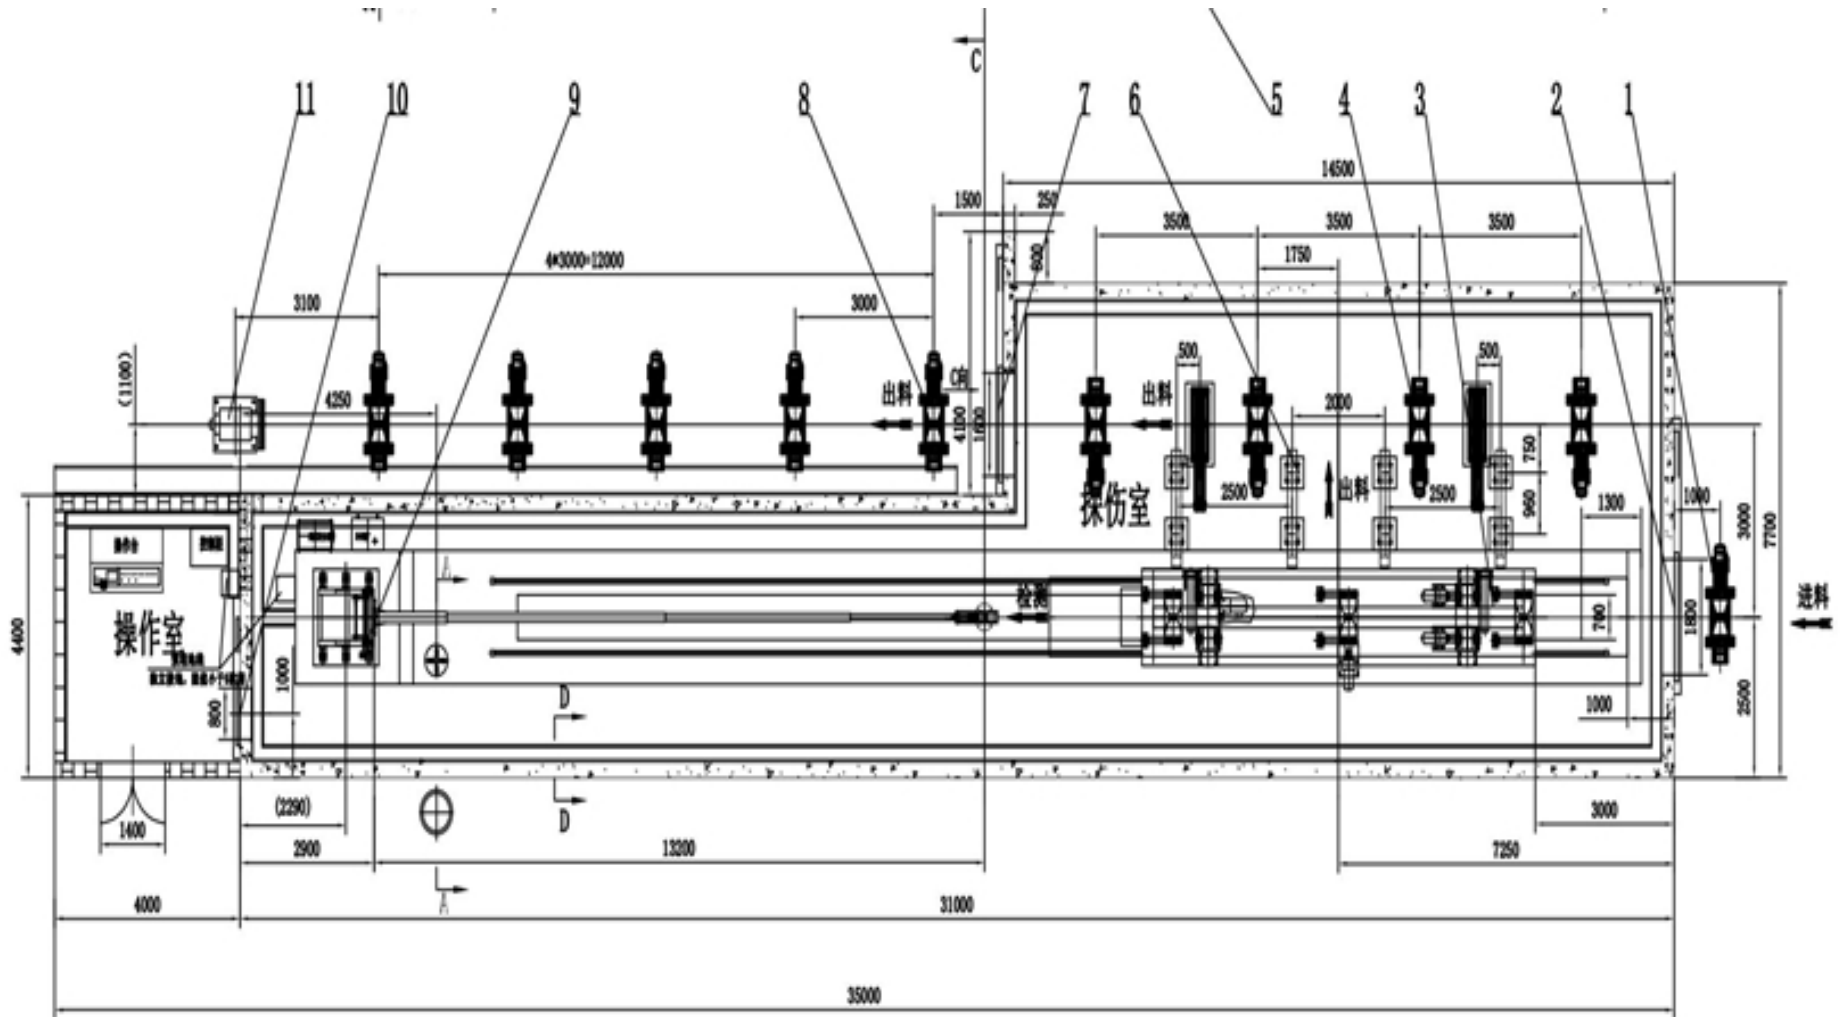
螺管一车间探伤室（X 射线实时成像检测系统）平面布置图
